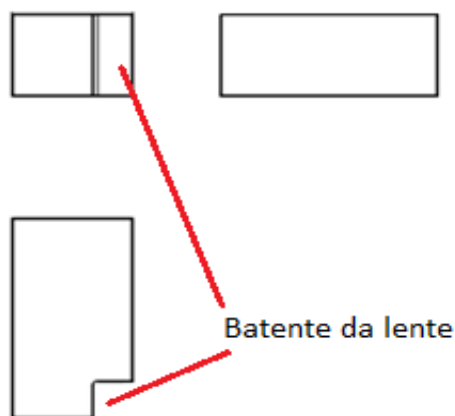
Desenho técnico de adaptador para inspeção do centro da lente.
